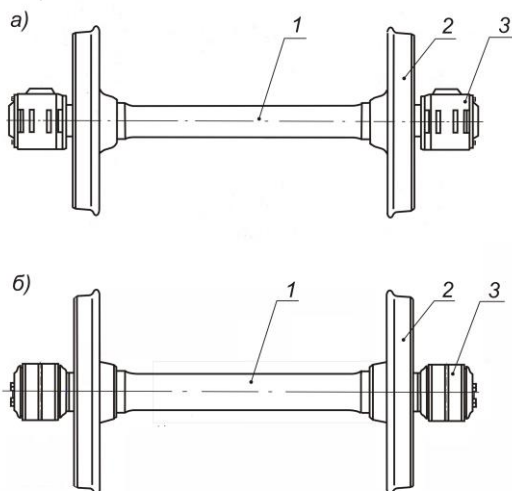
Колесная пара с неподвижно закрепленными колесами и буксовыми узлами
